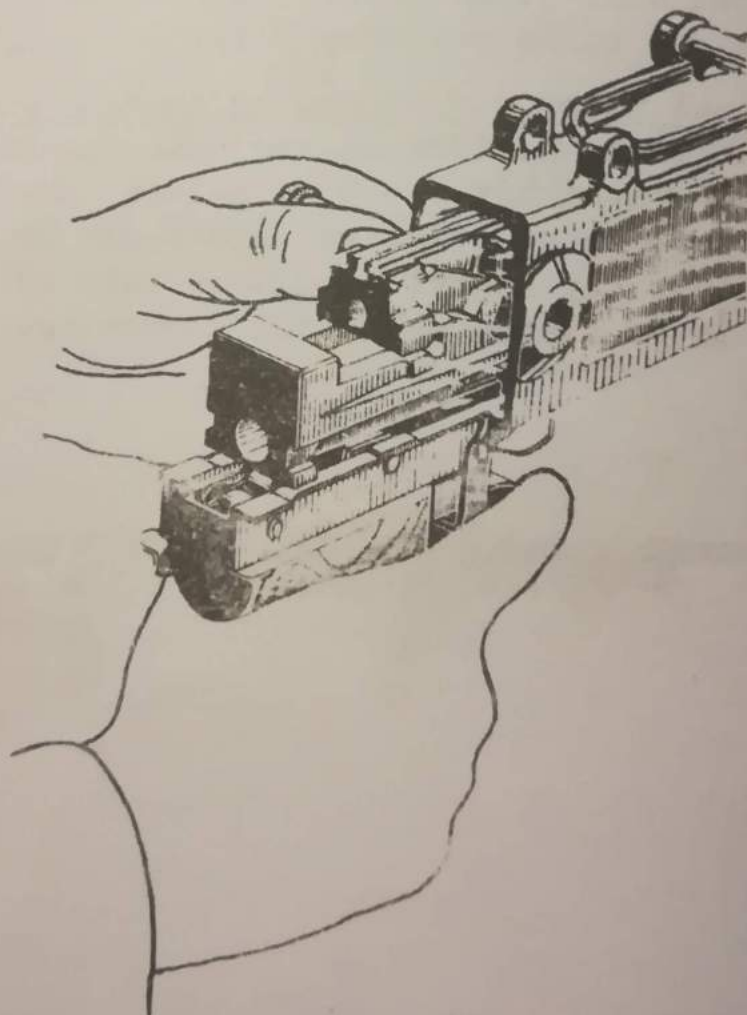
Oddělení pažby s uzávěrou od pouzdra závěru
